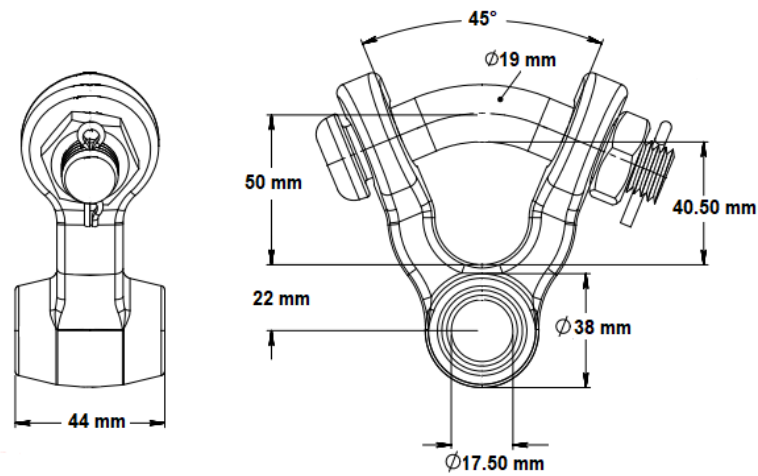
Detalle y dimensiones Horquilla-Ojo corta
